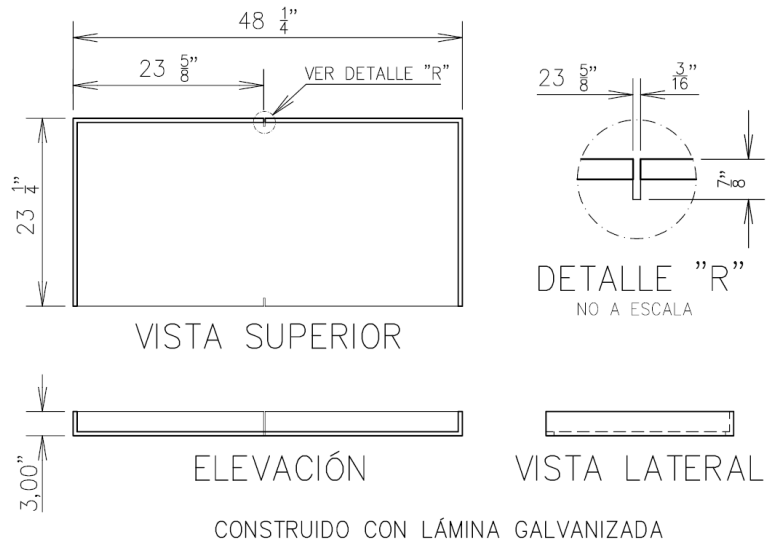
Parilla, banco de trabajo y base para entrepaño / soldadura
